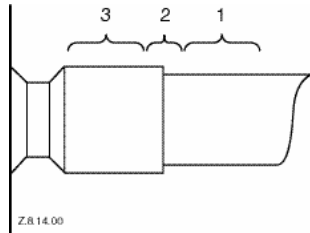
Áreas de soldadura del tubo de aspiración
